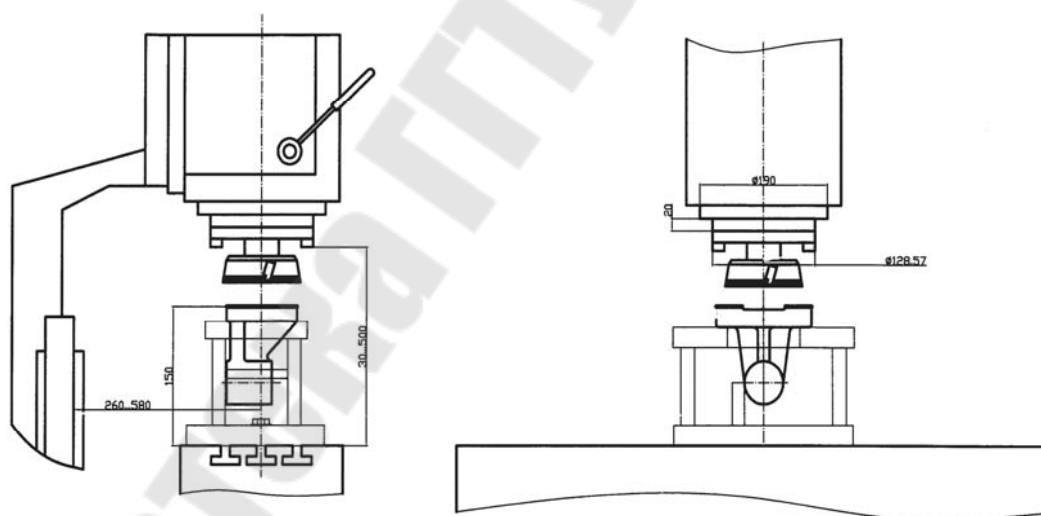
Эскиз рабочего пространства станка с обрабатываемой деталью
